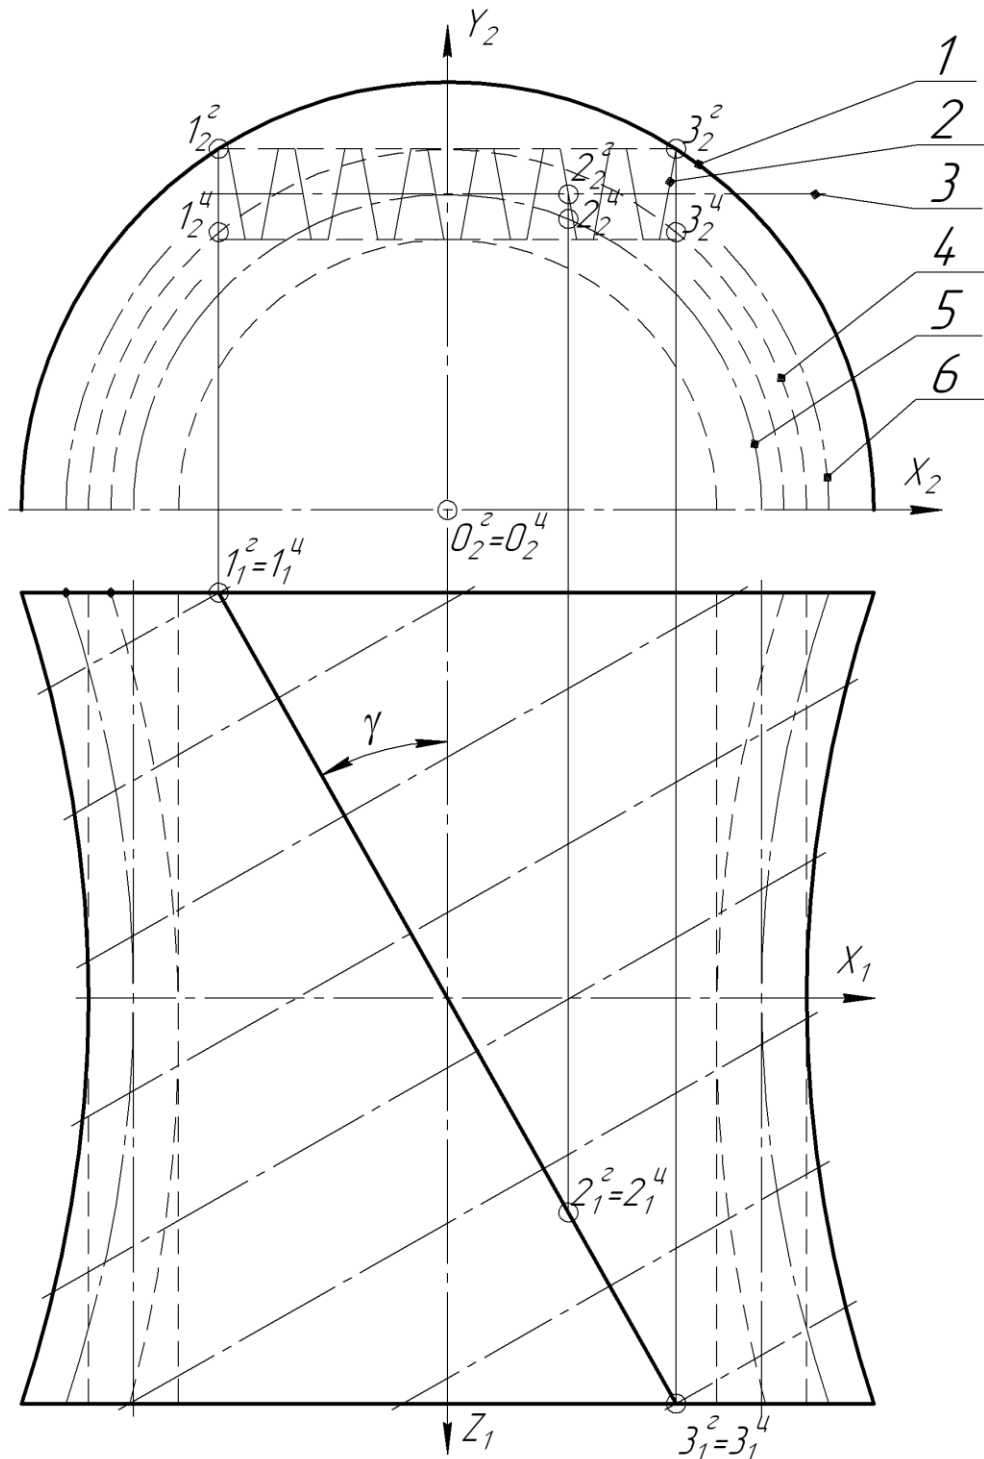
Связь зубьев зубчатой рейки с зубьями цилиндрического и гиперолоидного шлифовальных кругов:
